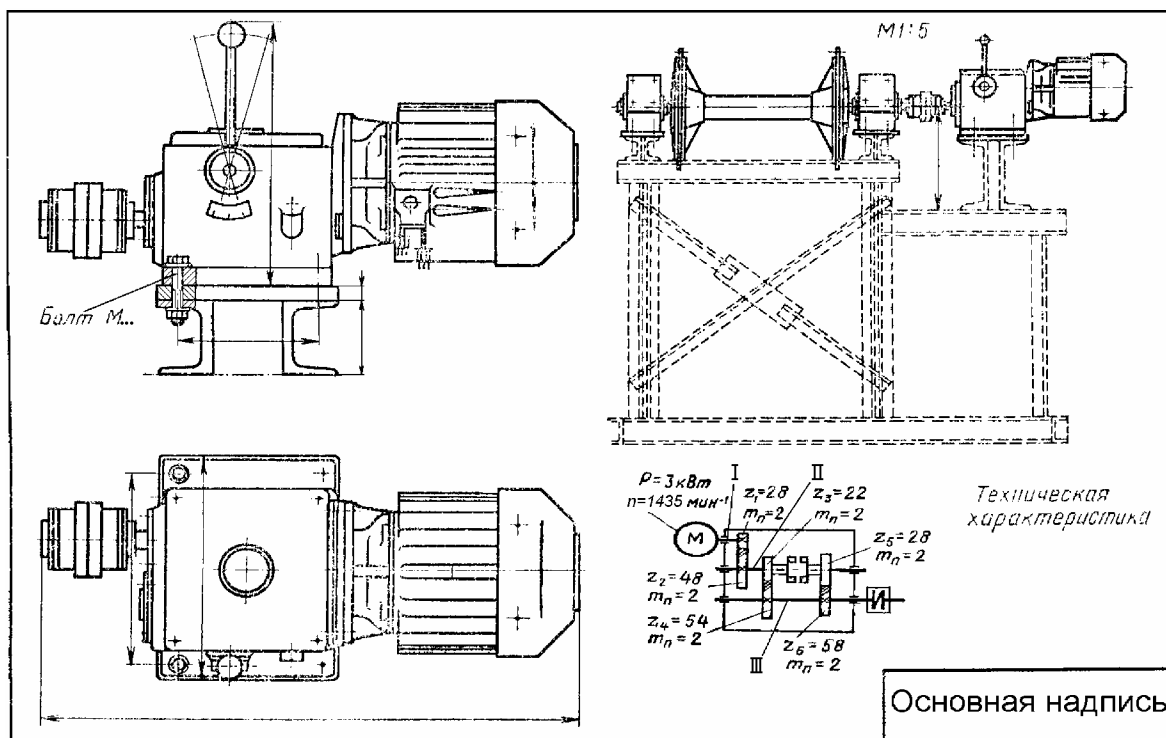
Общий вид привода цепного конвейера с установкой на сварной раме
